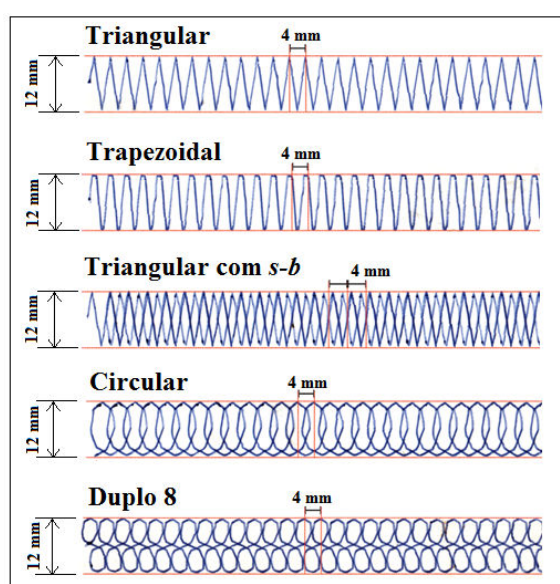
Resultados dos ensaios de movimentação com o manipulador de soldagem
